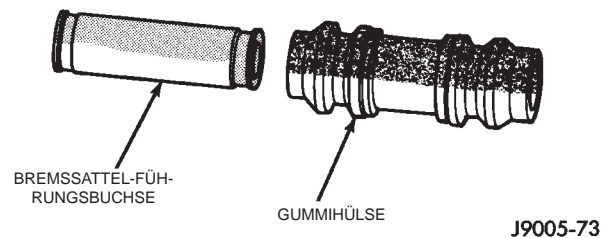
Führungsbuchse für Bremssattel-Befestigungsschraube und Gummihülse
